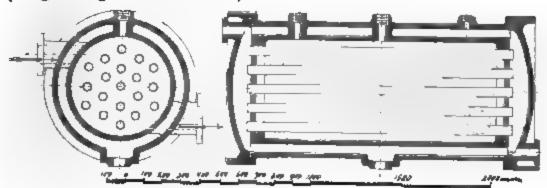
1566. Receiver für stehende Wasserwerksmaschine. d = 430, D = 660, H = 1000.
